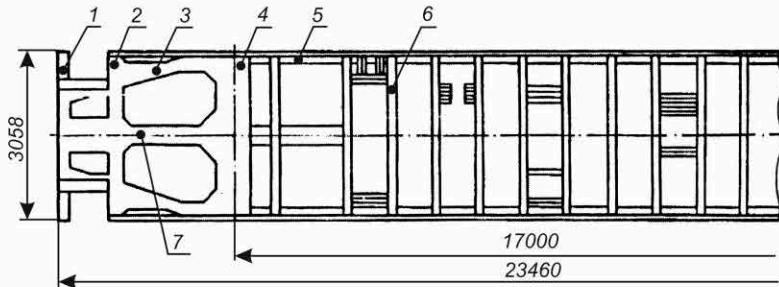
Схема рамы кузова пассажирского вагона без хребтовой балки
